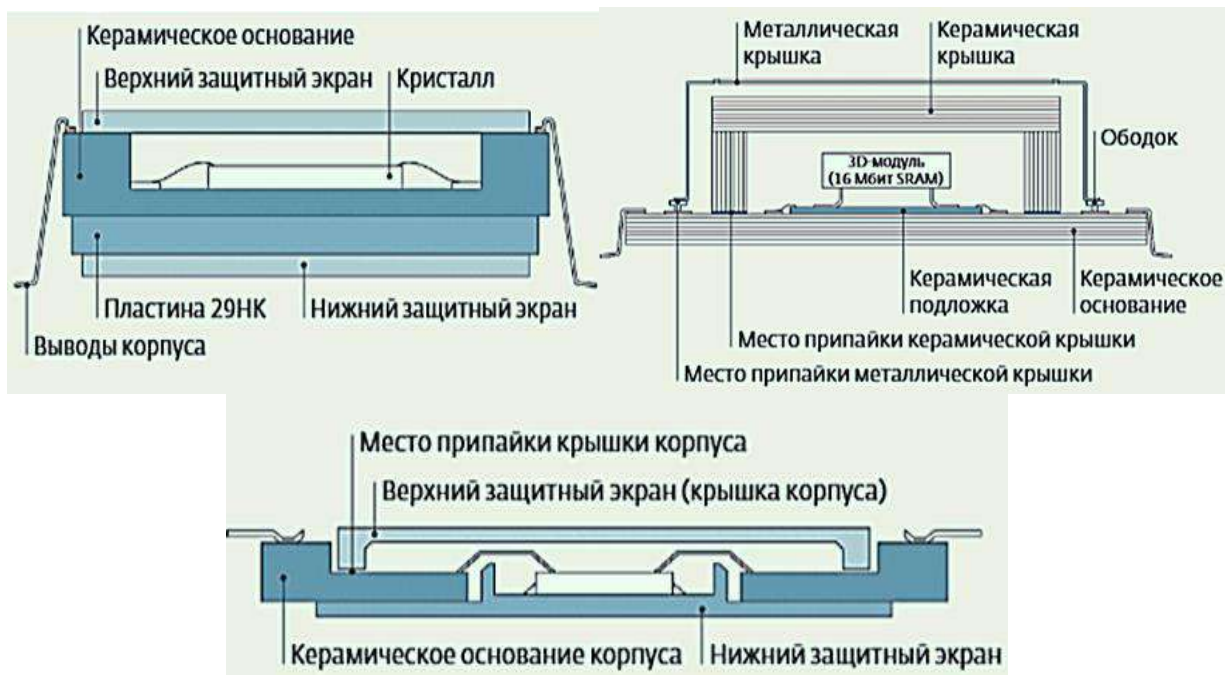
Конструкции корпусов ИМС с интегрированными ЭРЗ, используемые рядом зарубежных компаний
